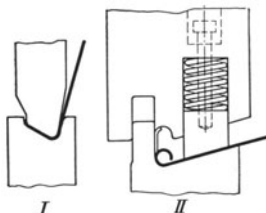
Anrollen unter 2 Rollwerkzeugen
